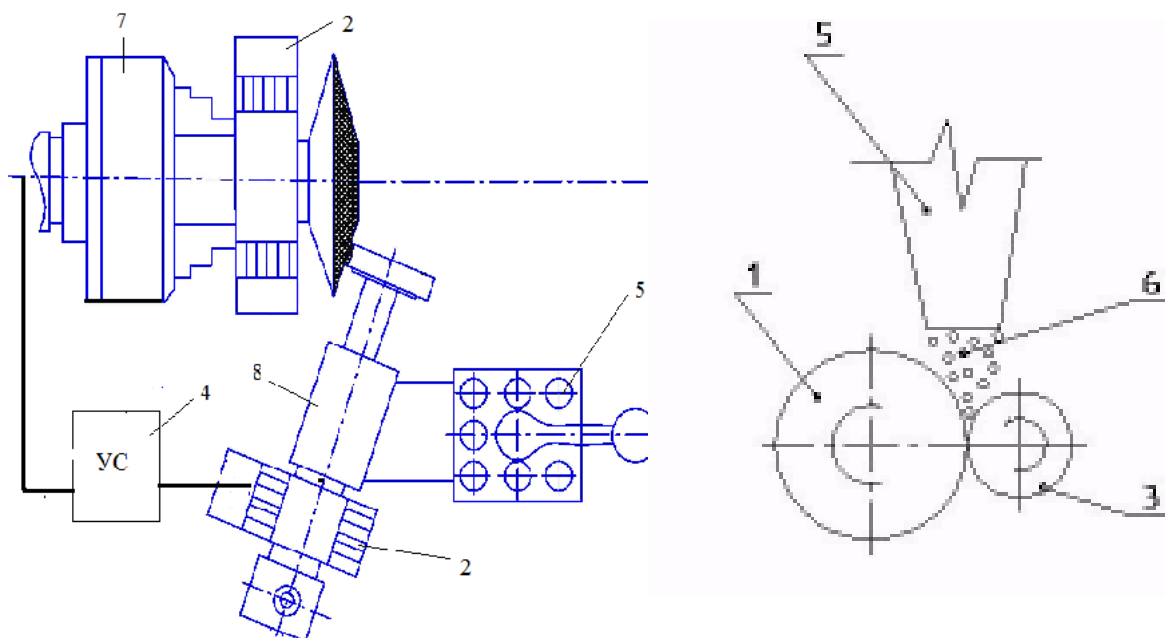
Схема установки электроконтактного спекания порошка на поверхности ролика. 1- деталь; 2- токосъемники; 3- ролик- электрод; 4- блок управления; 5- резцедержатель; 6-порошок; 7-трехкулачковый патрон; 8-механизм для создания усилия прижатия.
